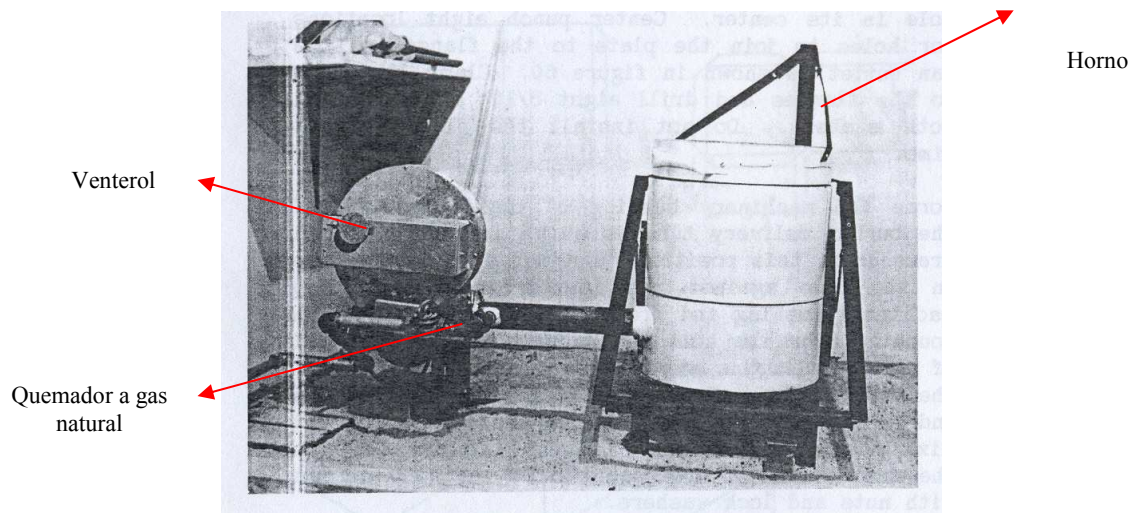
Horno de crisol y componentes, diseñado por D. Gingery
